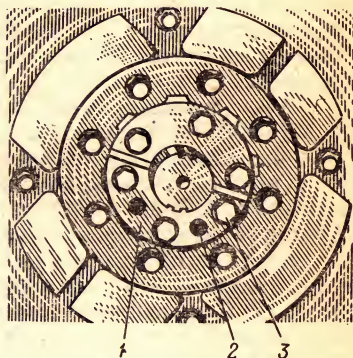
Крепление заднего колеса трактора ЮМЗ-6: 1 — вкладыш; 2 — резьбовые отверстия для демонтированных болтов; 3 — болт
